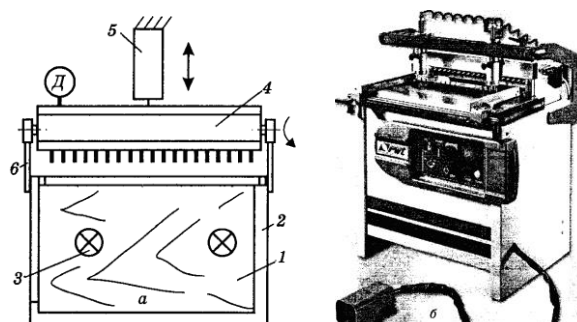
Позиційний багатошпиндельний вертикально-горизонтально свердлильний присадний верстат з однією головкою: а – принципова схема; б – загальний вигляд; 1 – щитова деталь; 2 – стіл; 3 – притискачі; 4 – багатошпиндельна головка; 5 – привод; 6 – кронштейни
